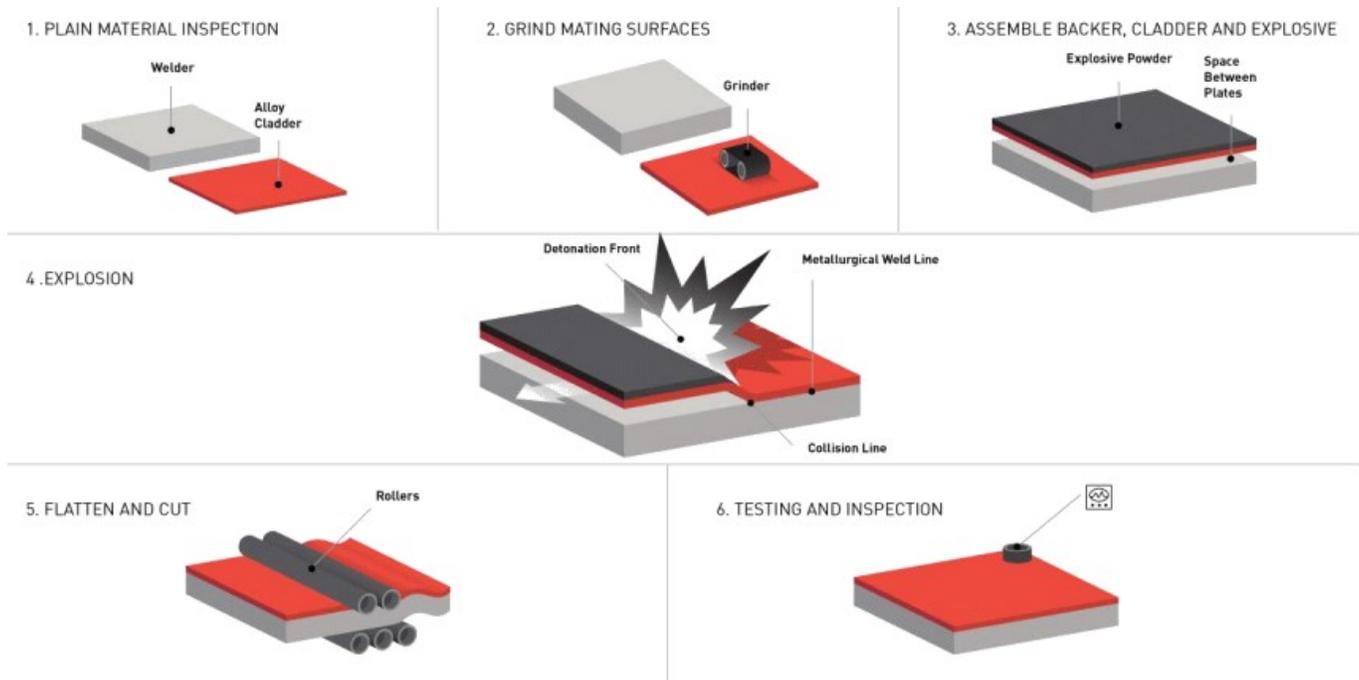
Proceso de soldadura mediante explosivos.
